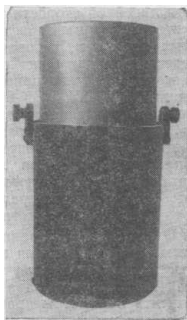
Оболочковая заготовка в термостампе для проведения термопрессовки
